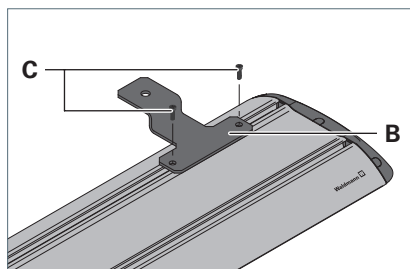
Montage de l'équerre pour le type de montage « En haut, fixe », possibilité 2.
